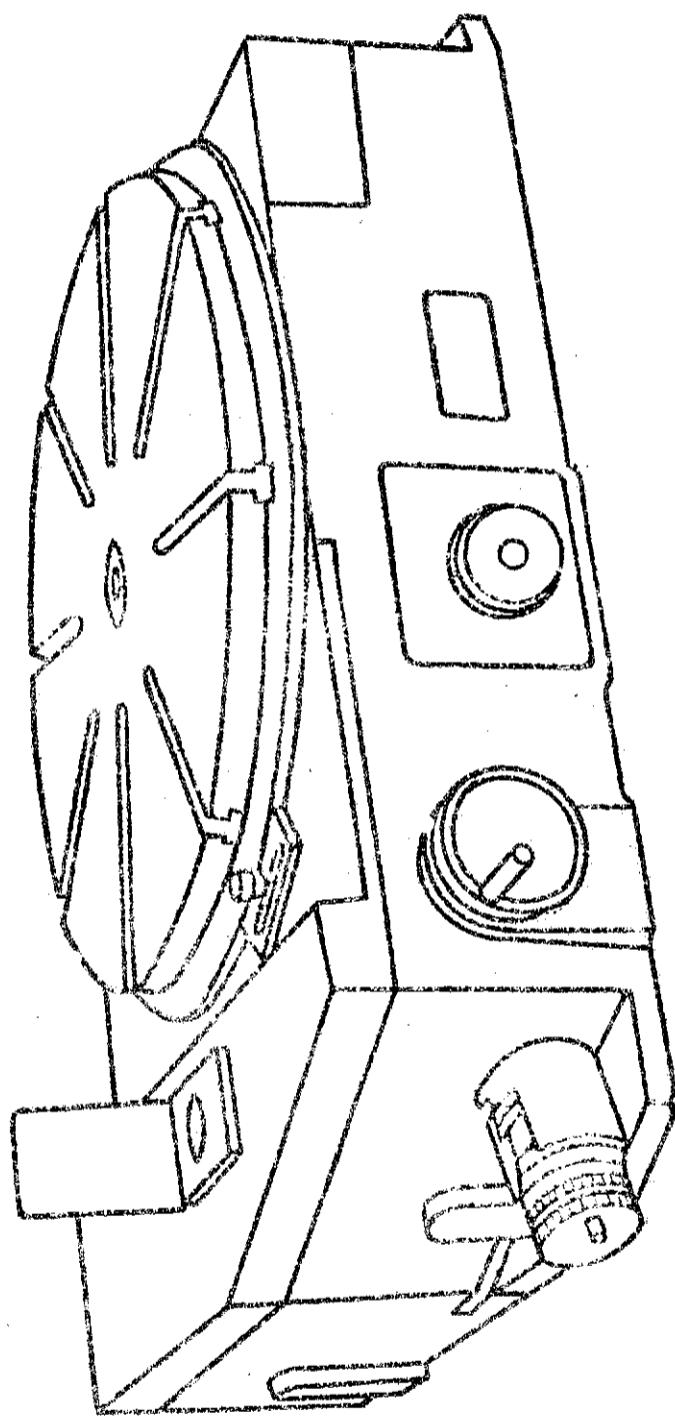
Рис. I. Стол простой поворотный дельтительный координатно-расточечный станка.
